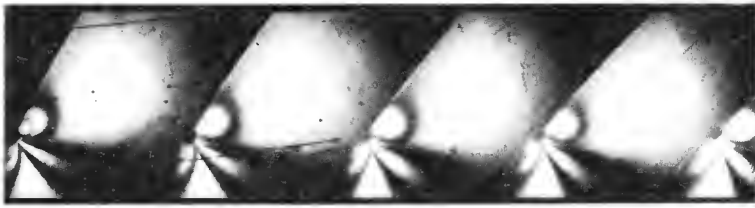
Spannungsoptische Aufnahmen vor einer Drehstahlschneide (nach F. Schwerd und P. Dietrich)
